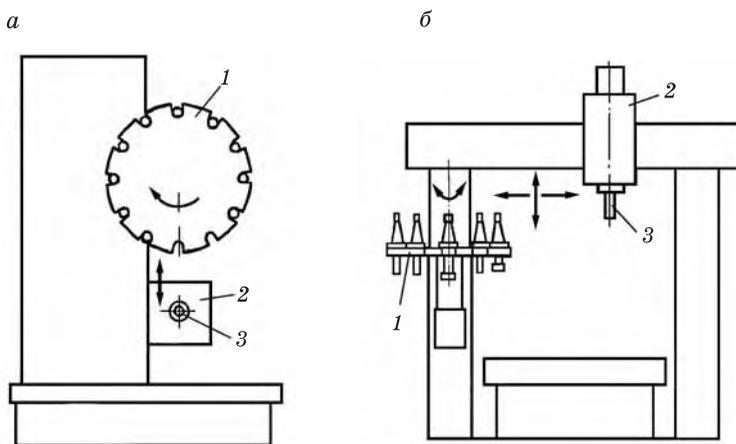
Смена инструмента при параллельном расположении шпинделя и магазина
